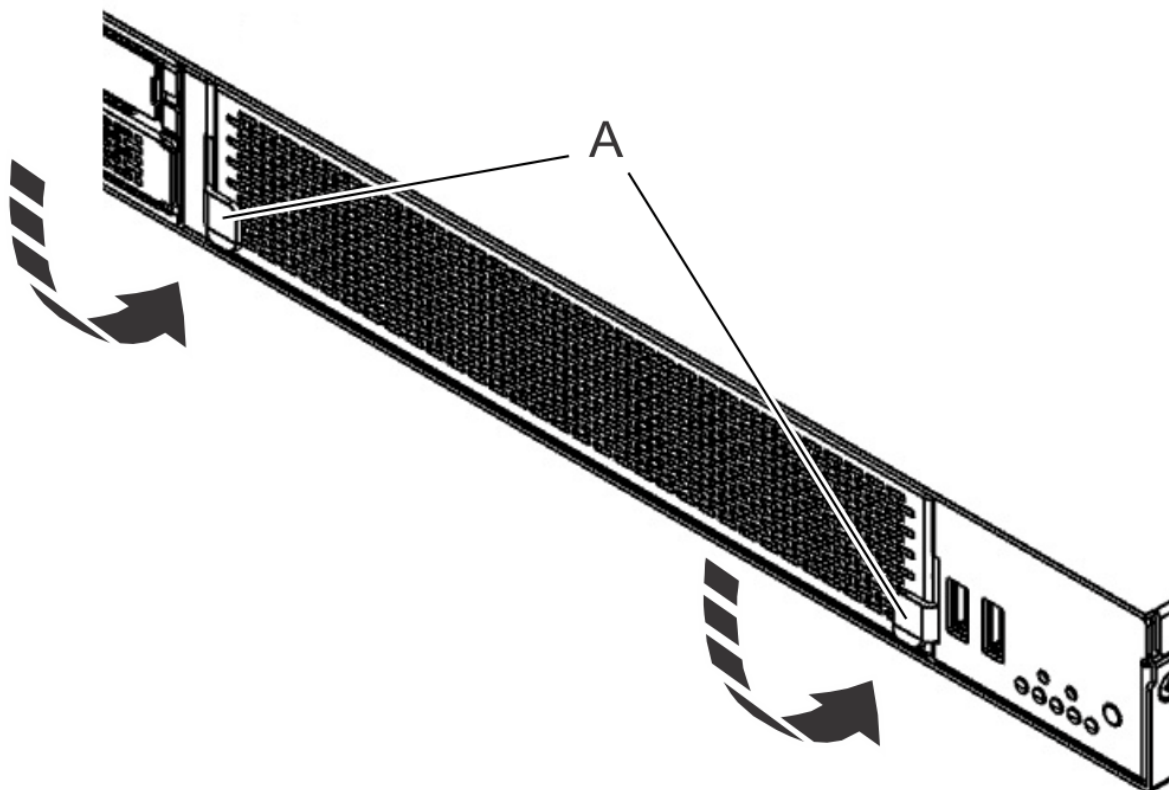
Dokręcanie bocznych wkrętów panelu operatora
